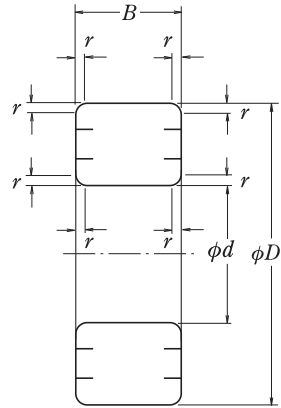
Dimensiones Globales para Rodamientos de Bolas y de Rodillos
